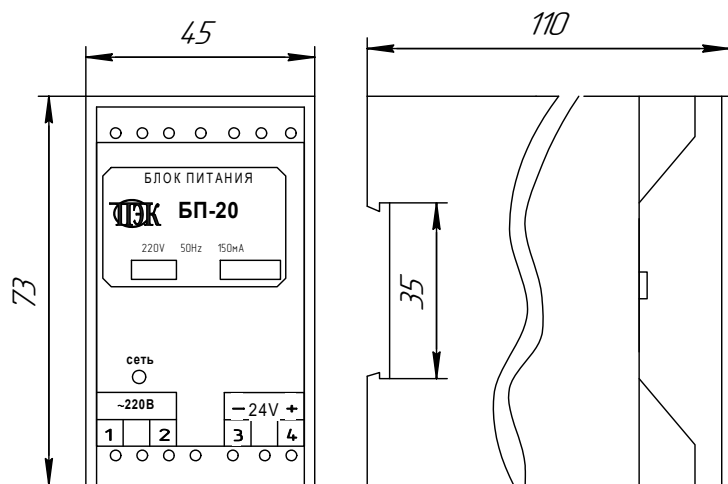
Габаритные размеры блока БП-20 на DIN-рейке
